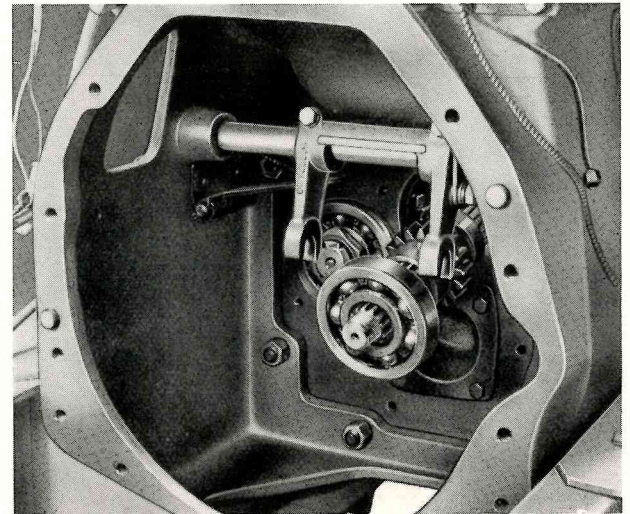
Smontaggio dell'albero con ingranaggi conduttori.
